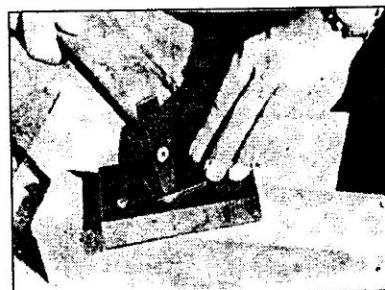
Рихтовка детали вокруг головки «заклепки»
